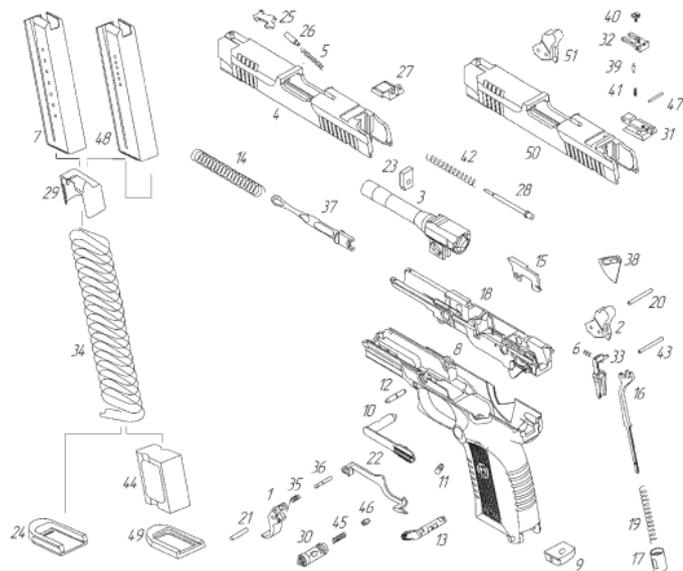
Схема сборочных единиц и деталей пистолета MP-446 VIKING с пластмассовым корпусом
